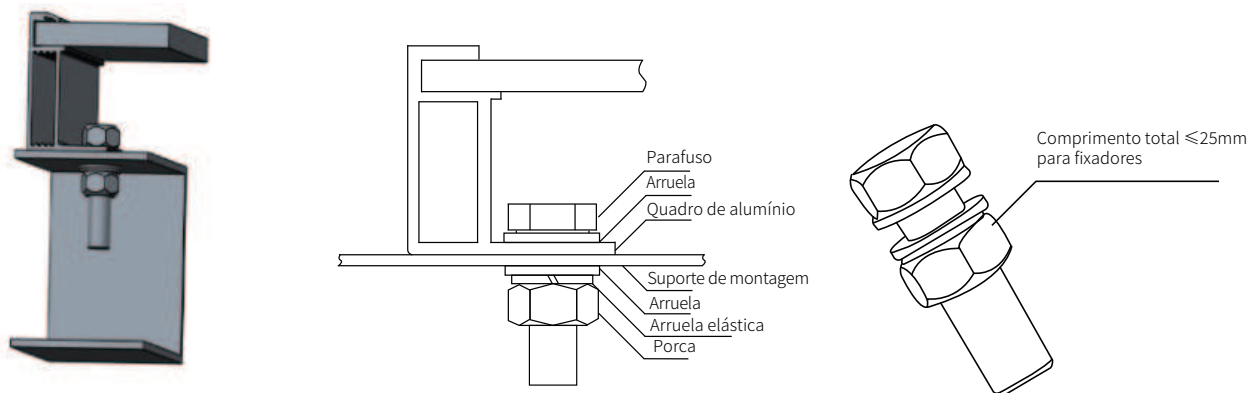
Ilustração de instalação de furo de montagem de módulo monofacial
